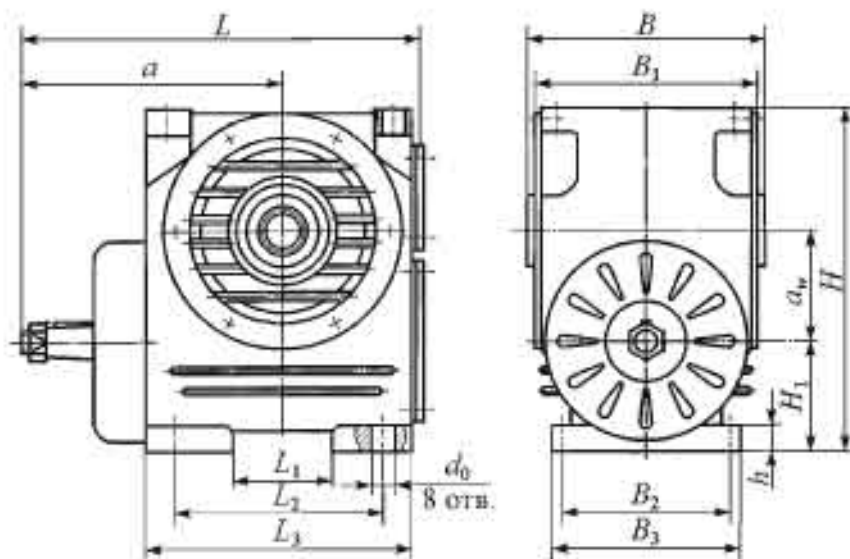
Габаритные, установочные и присоединительные размеры червячного редуктора
